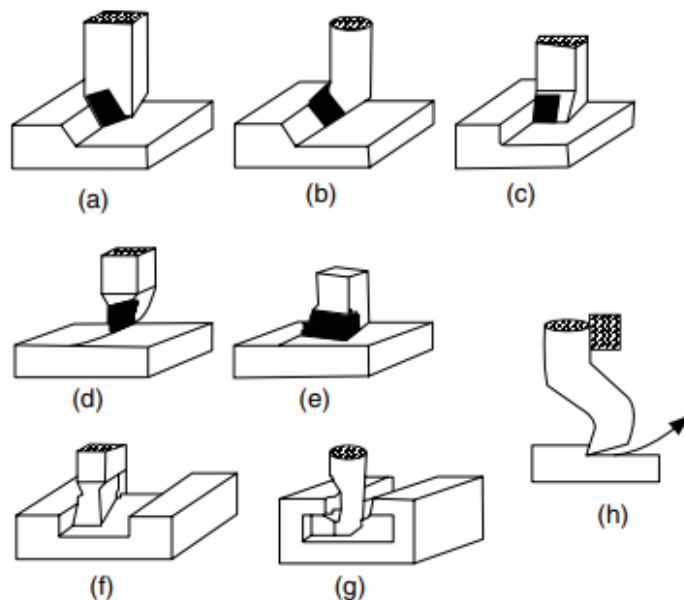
Типові інструменти, що використовуються при довбанні [12]
